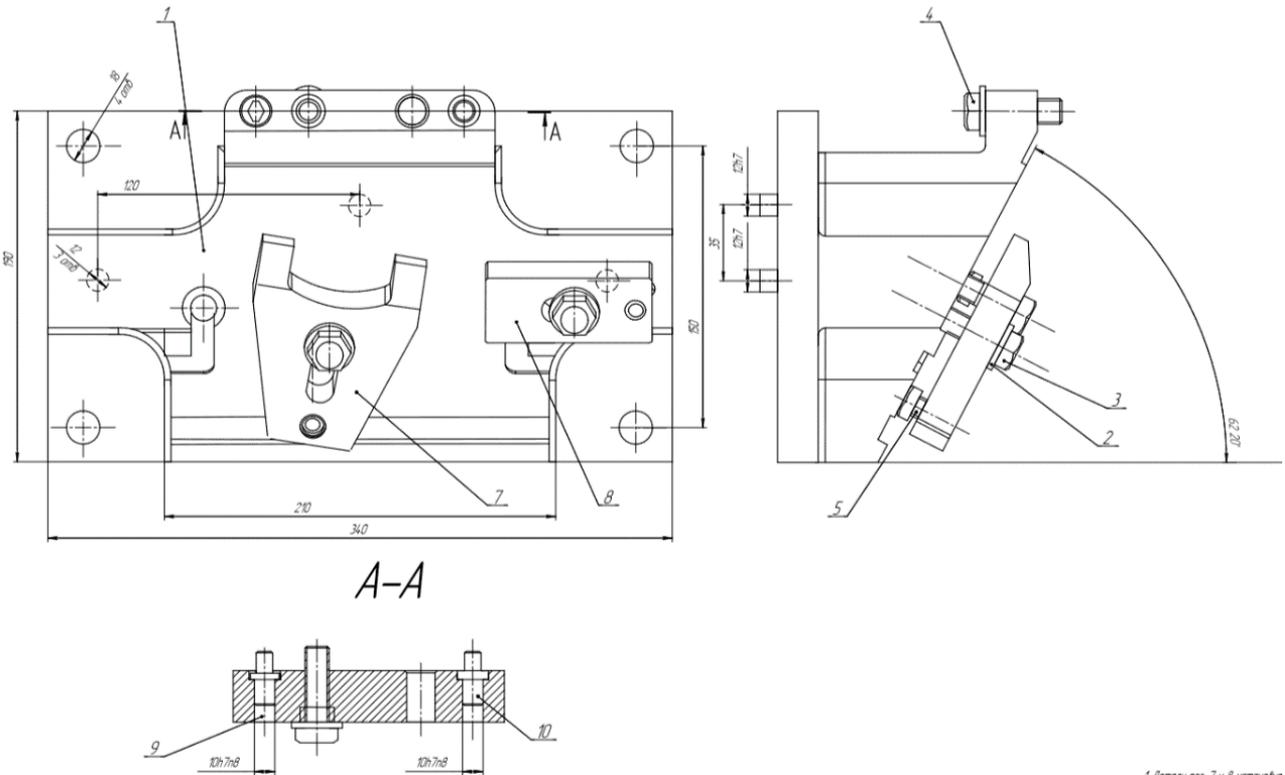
Эскиз установки заготовки в специальное фрезерное приспособление
